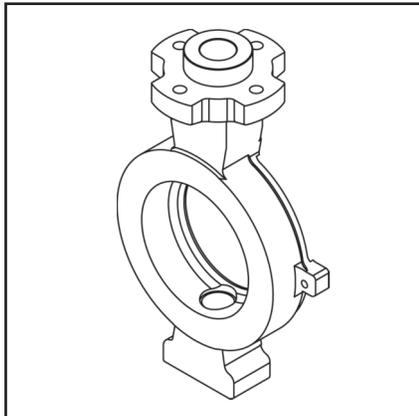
Vista Explodida do Subconjunto do Corpo
